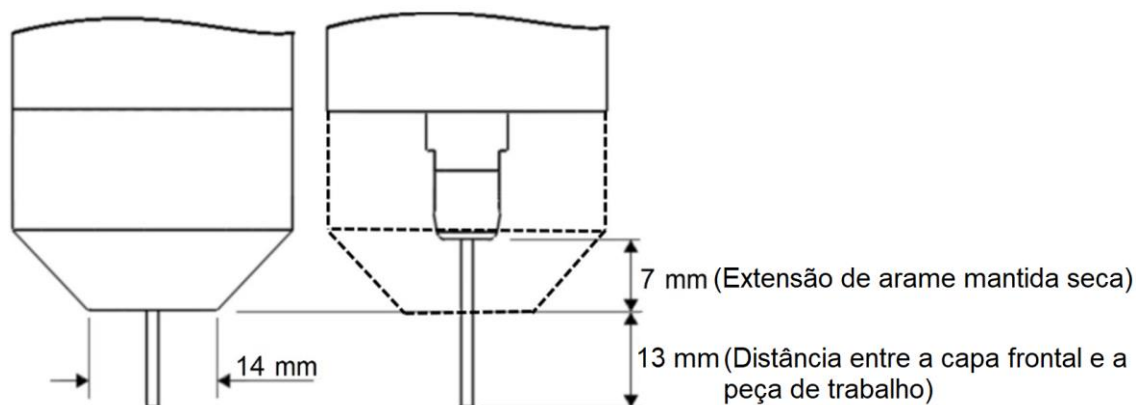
Comprimento mínimo de arame mantido seco e dimensões da tocha de soldagem.
